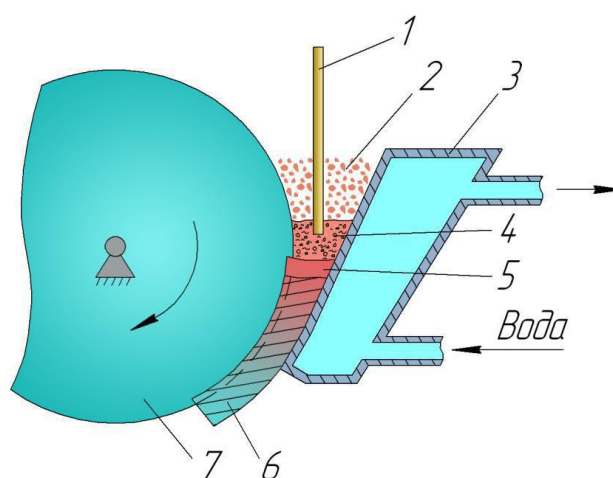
Схема выполнения электрошлаковой наплавки
